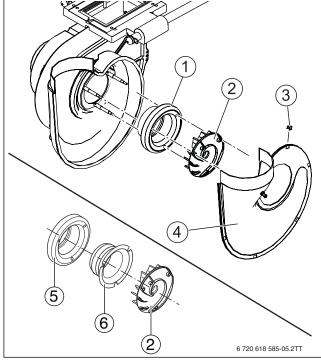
Smontaggio dei componenti del collettore di ventilazione
